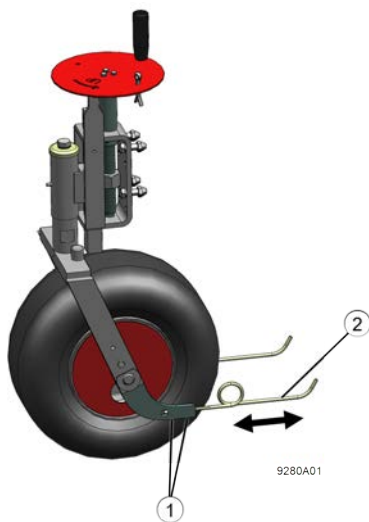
Réglages possibles des tiges de guidage en forme de queue de cochon de la roue de jauge
